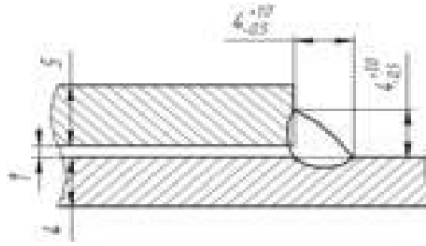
Схема зварного шва для механізованого зварювання у суміші захисних газів
